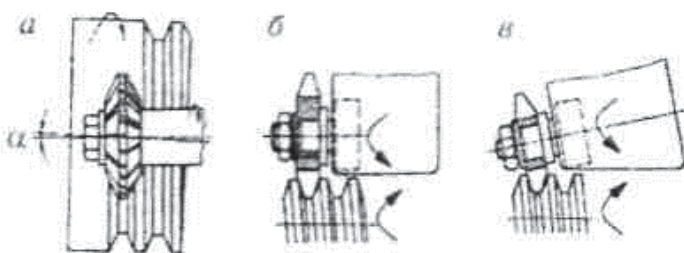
Схемы фрезерования резьбы дисковыми фрезами: а – смещение осей фрезы и нарезаемой детали; б – фреза симметричного профиля; в – фреза несимметричного профиля
